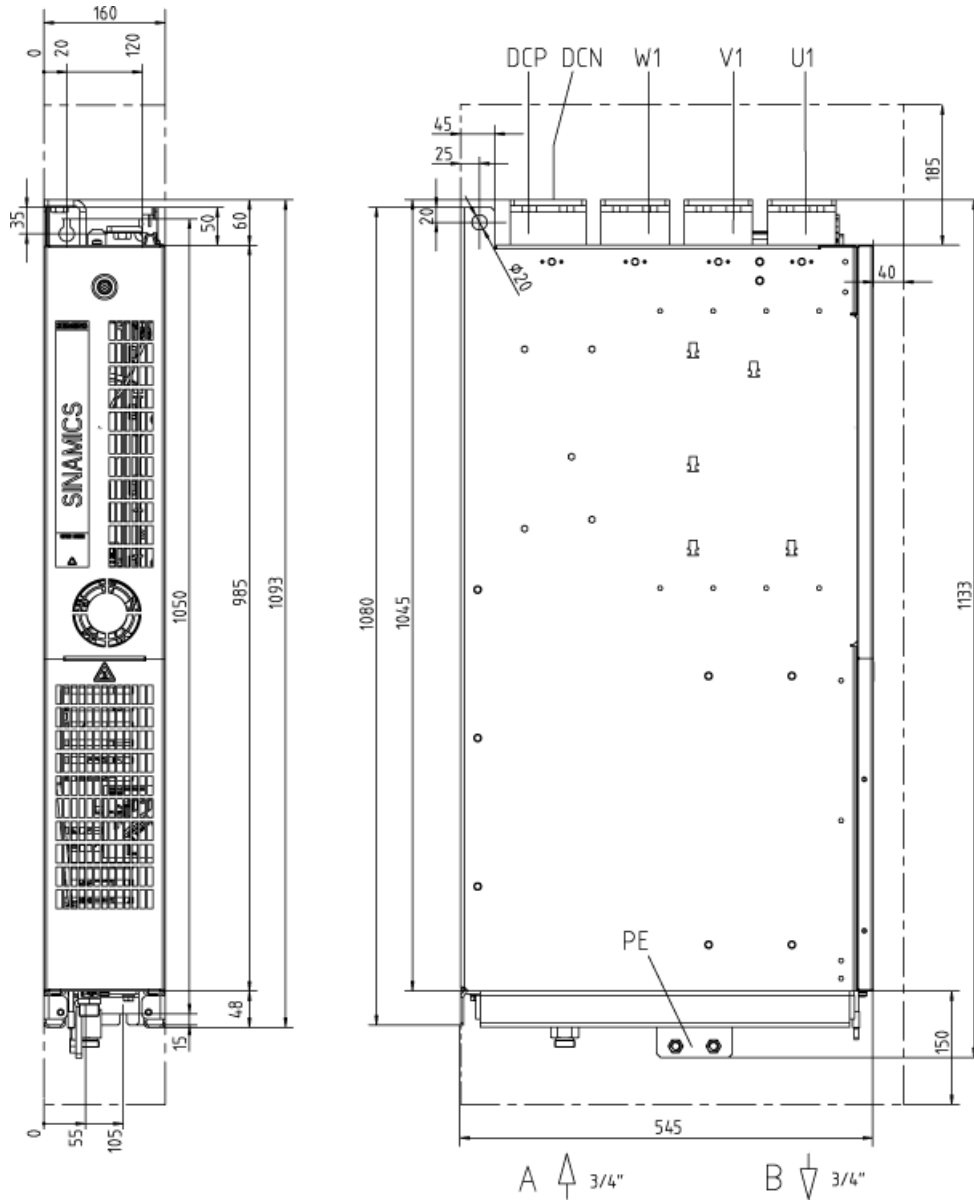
Габаритный чертеж, модуль питания Basic, типоразмер FBL. Вид спереди, вид сбоку
